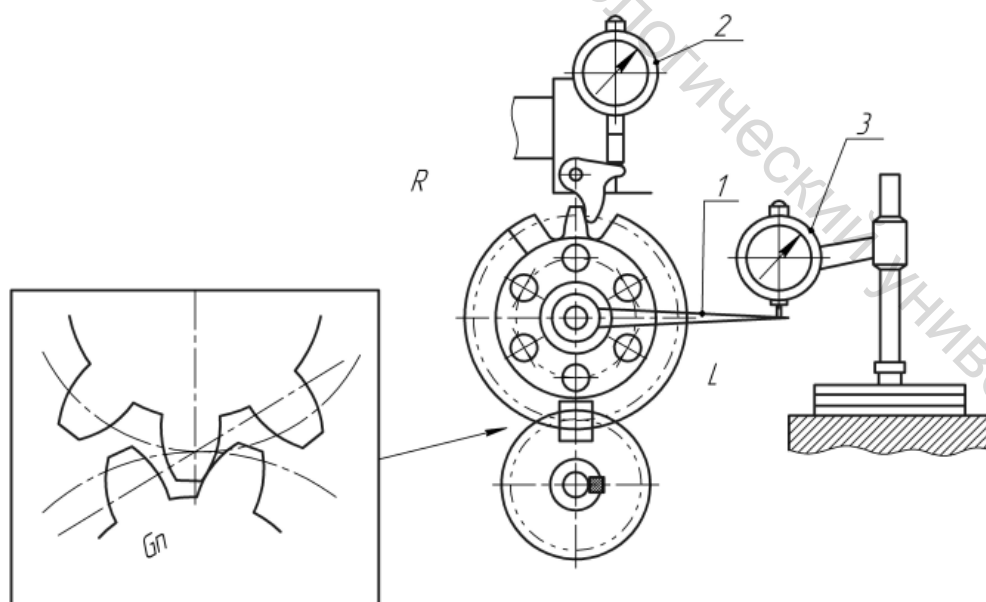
Схемы контроля зазора в зацеплении зубчатых колес
